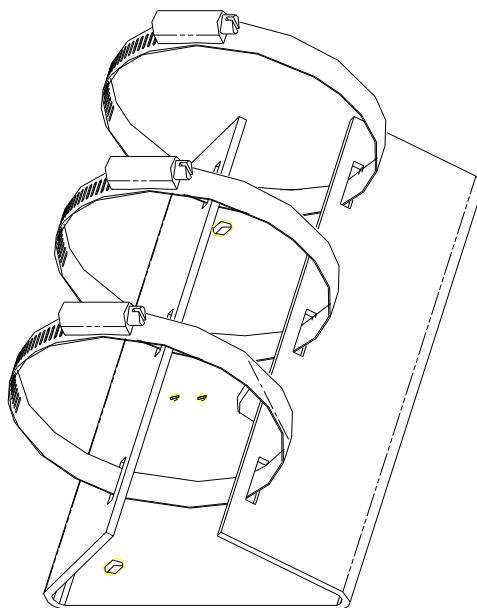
16 Anbringen der Bänder am Mastadapter
